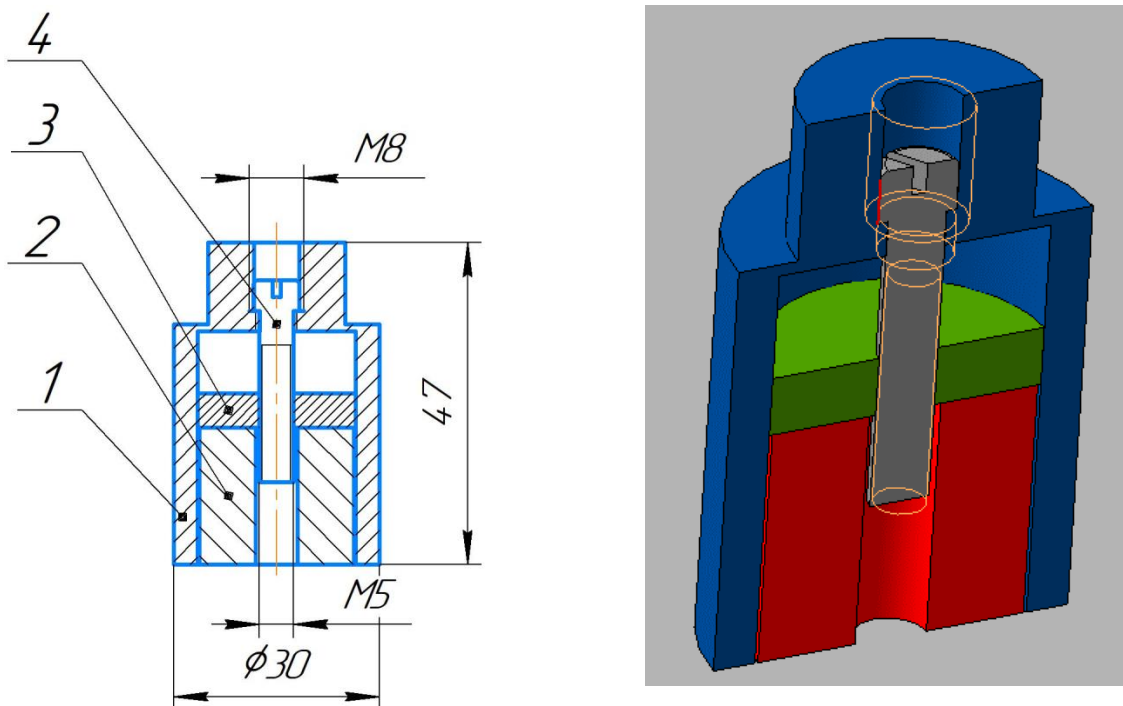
Магнітний захват : 1 – стакан; 2 – магніт Nd - Fe - В марки №38;
